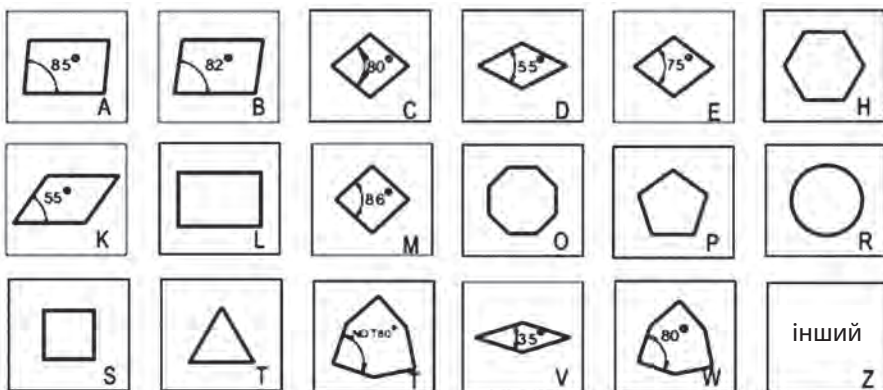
Твердосплавні пластини для напайки на токарні різці
